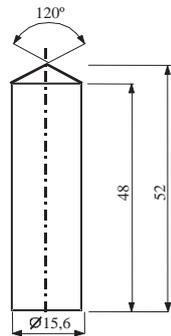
Piston cylindrique en bronze, dimensions en mm
